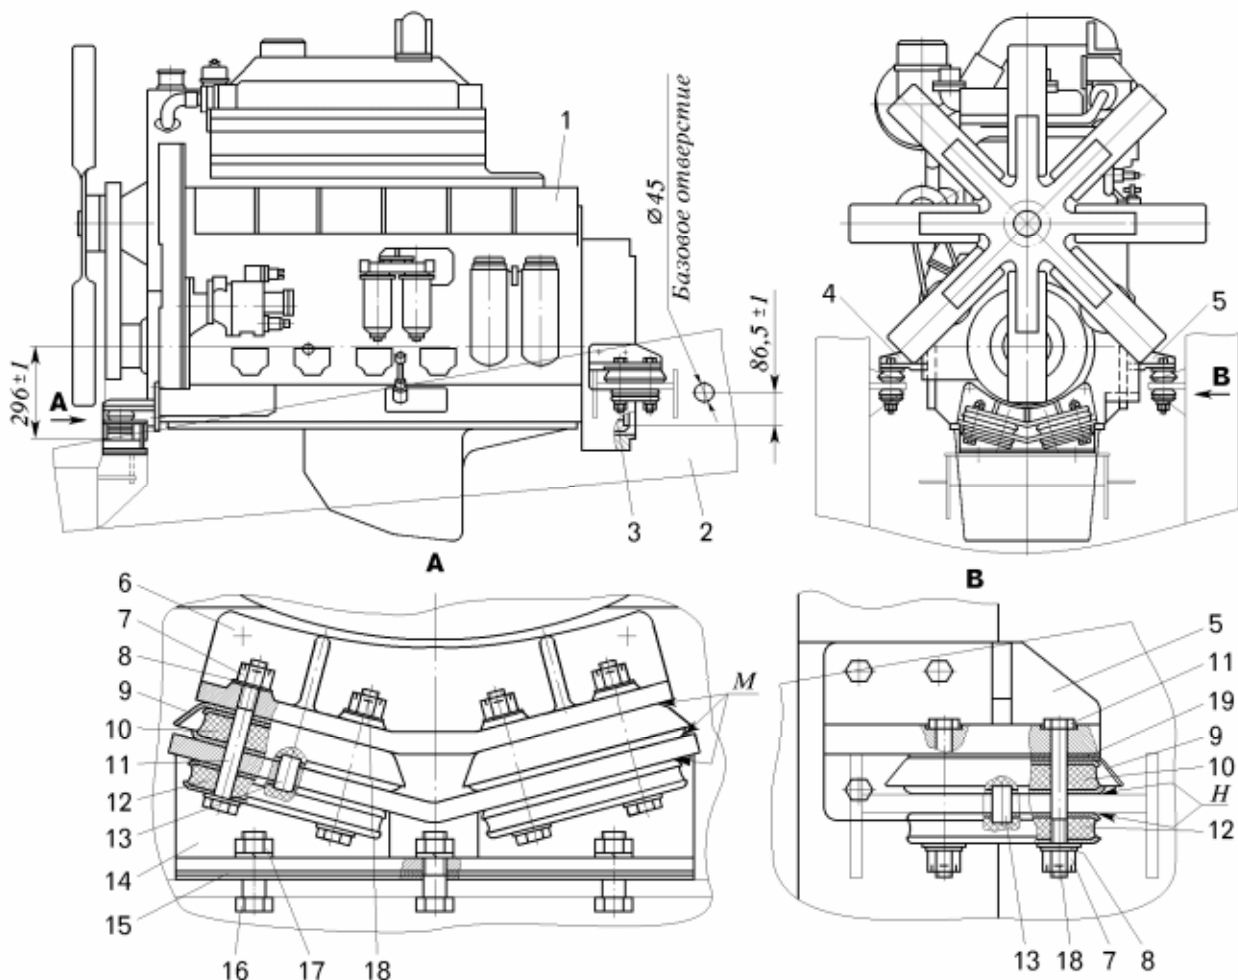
Установка двигателя самосвала БелАЗ-7555В:
